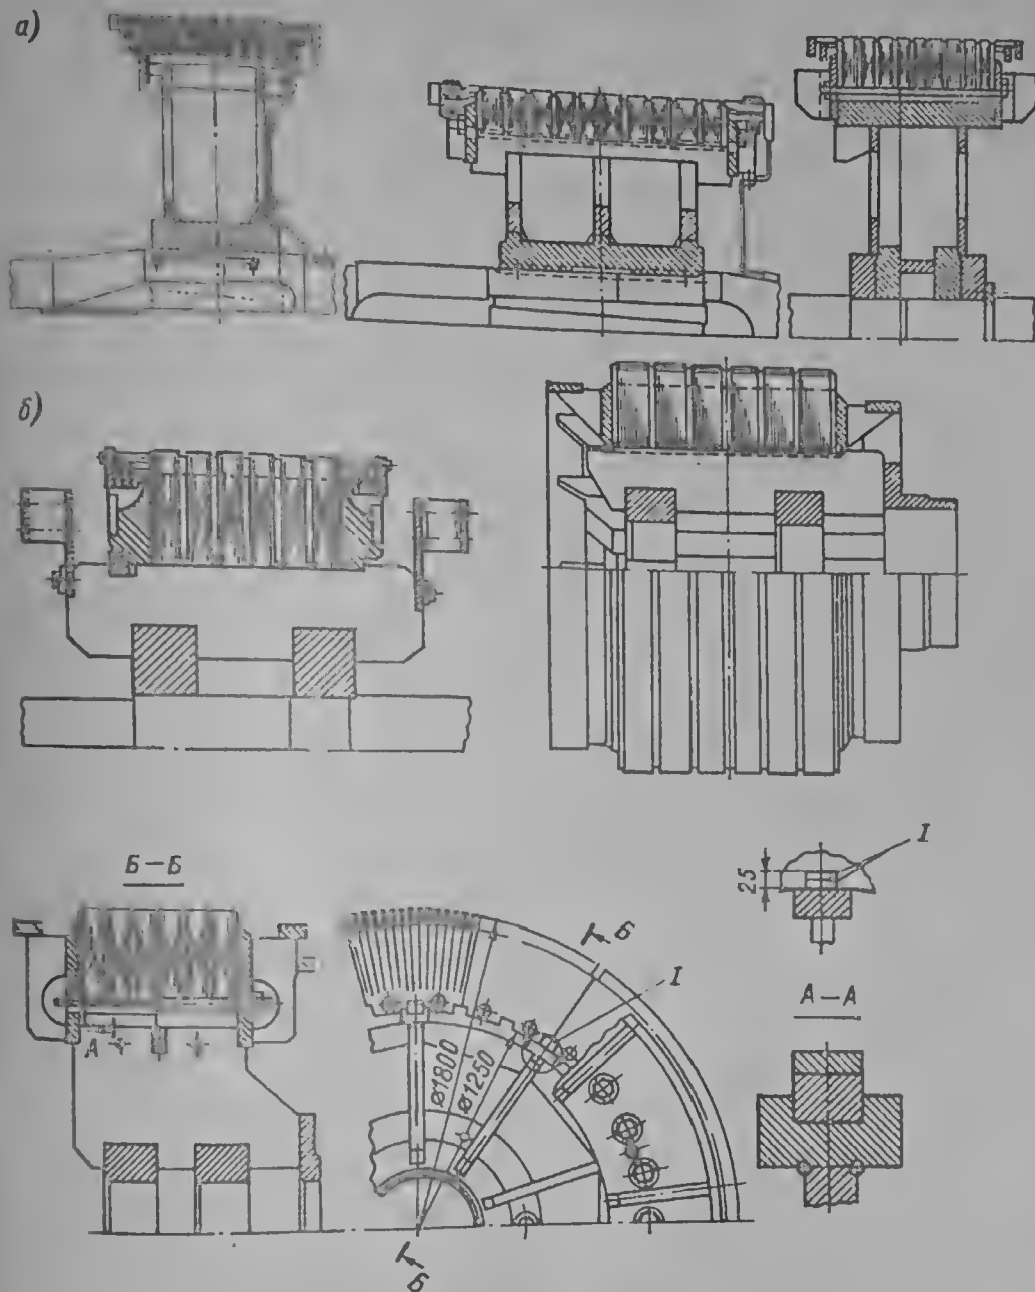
Конструкции роторов машин переменного тока: а — с остовами в виде двух- и трехдискового барабана; б — с остовом из ребер и колец
